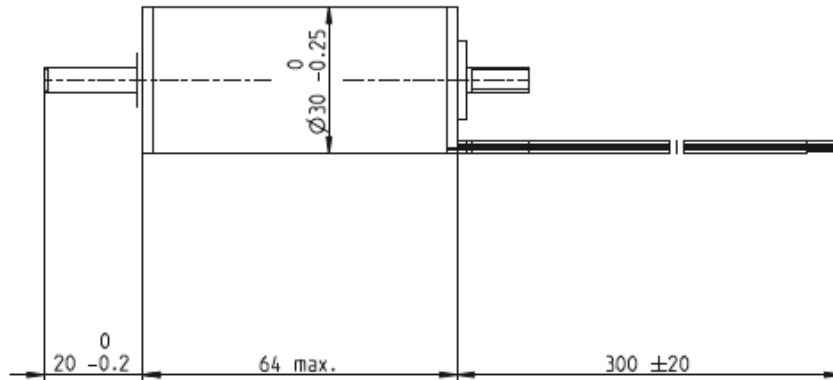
Principais dimensões do motor selecionado. Adaptado de [31].
